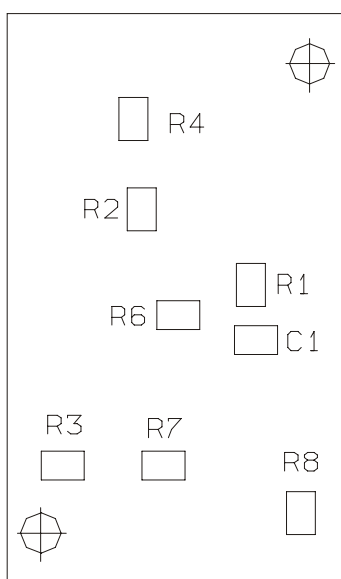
Сборочный чертеж платы искрозащиты блока датчика СКГГ варианта исполнения 1. Сторона пайки.
